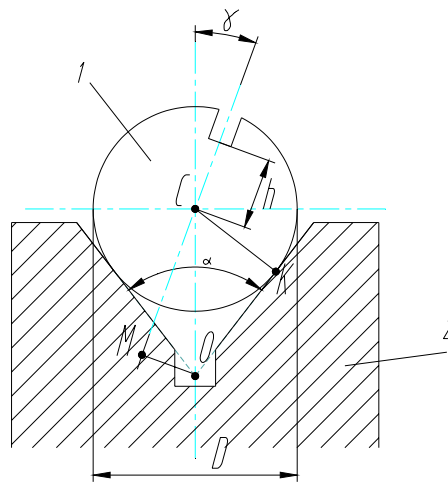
Исходные данные для расчета действительной погрешности базирования при установке заготовки в призме: 1 - заготовка; 2 - призма.
